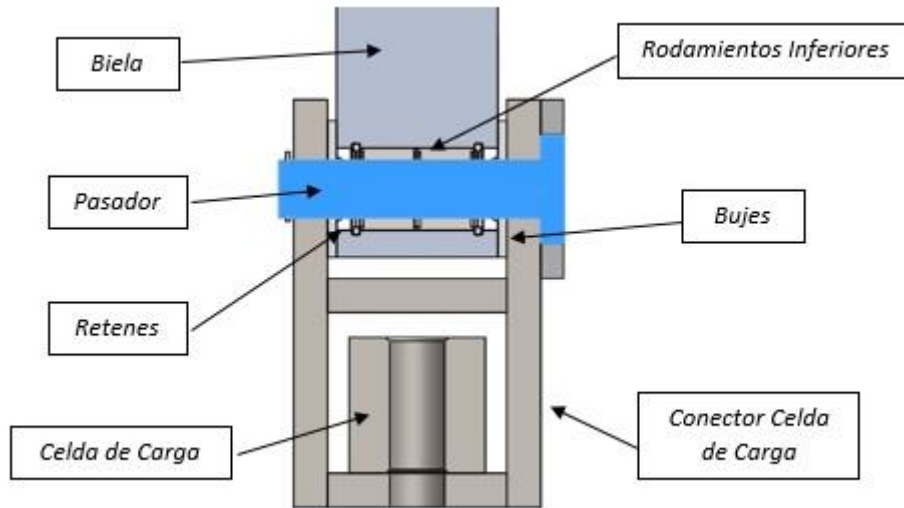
Vista en corte conjunto conexión celda de carga
